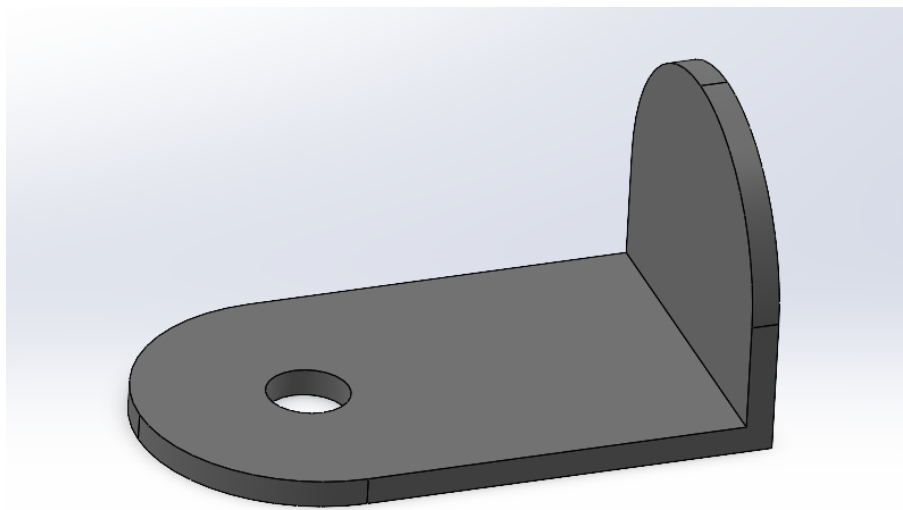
Diseño en SolidWorks de la pieza que va soldada a la estructura tubular para amarrar la barra de torretas al chasis.
